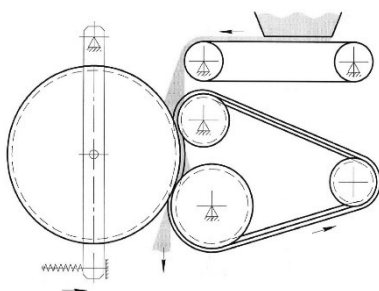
Схема тривалкової дробарки згідно з пат. № RU 2571059C1
